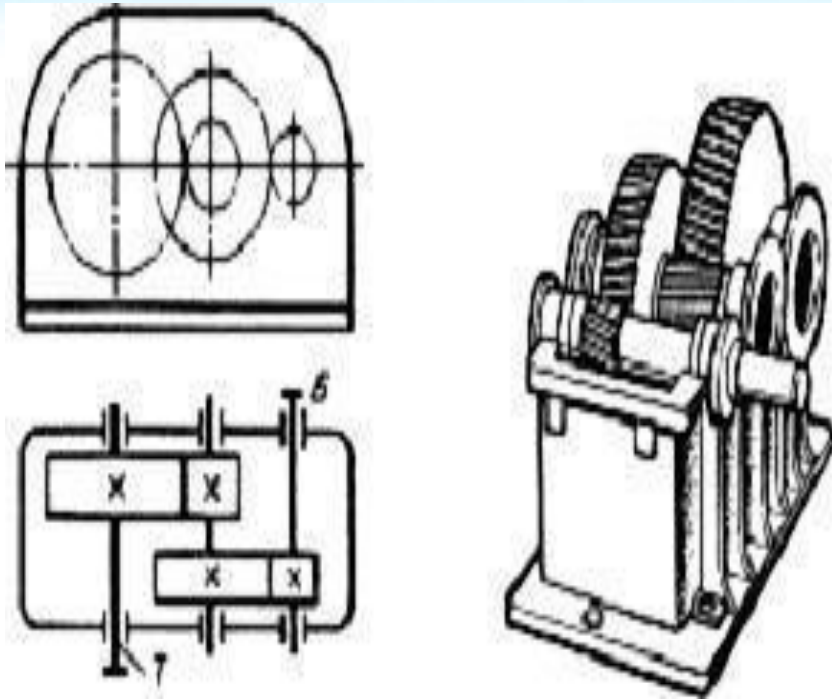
а - Двухступенчатый цилиндрический редуктор горизонтальный
